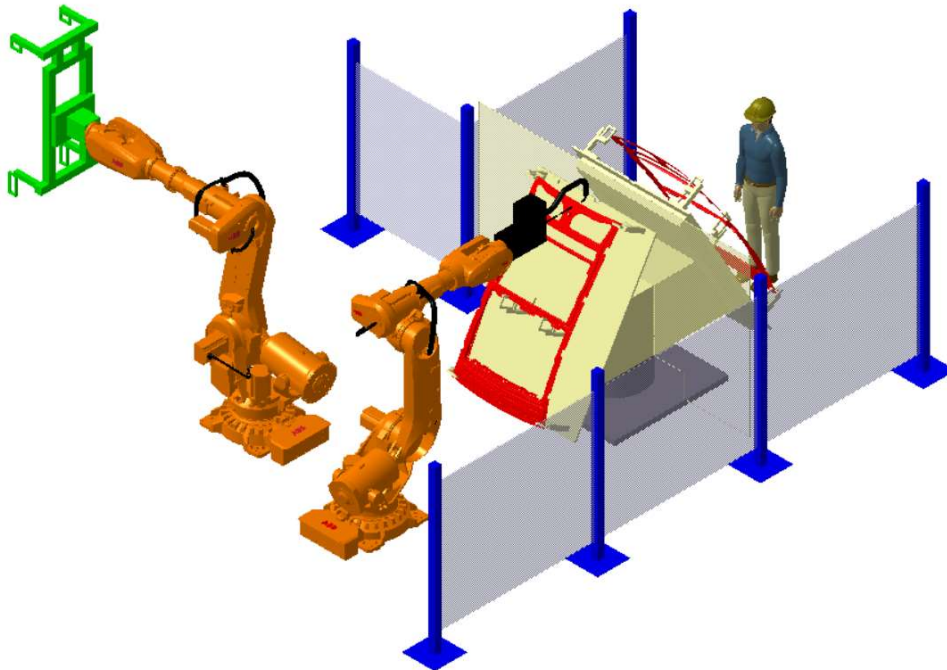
Umístění otočného stolu s přípravkem, robota pro svařování a obsluhy
